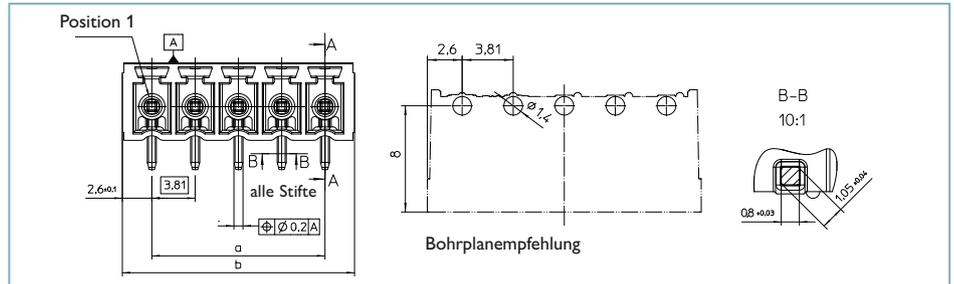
Layout- und Toleranzzeichnung eines typischen THR-Bauteils
